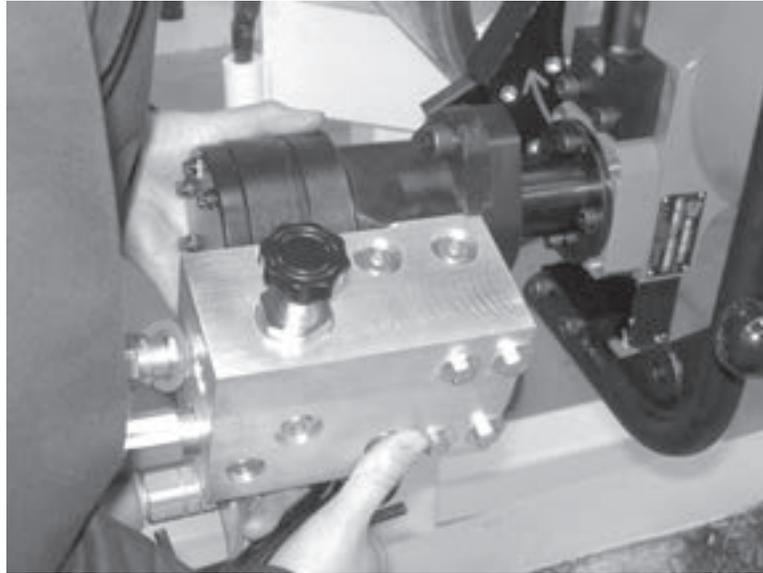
Monte la brida del motor hidráulico sobre los tornillos en el adaptador de motor.
